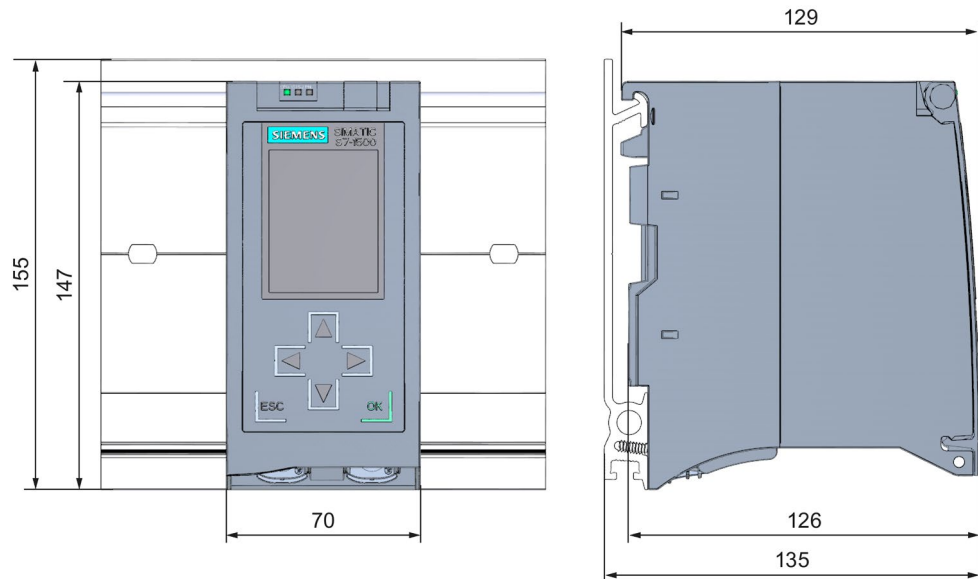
Dessin coté de la CPU 1515-2 PN, vue de face et vue latérale
